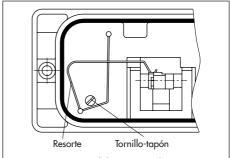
Montaje del resorte en la parte posterior de la carcasa
